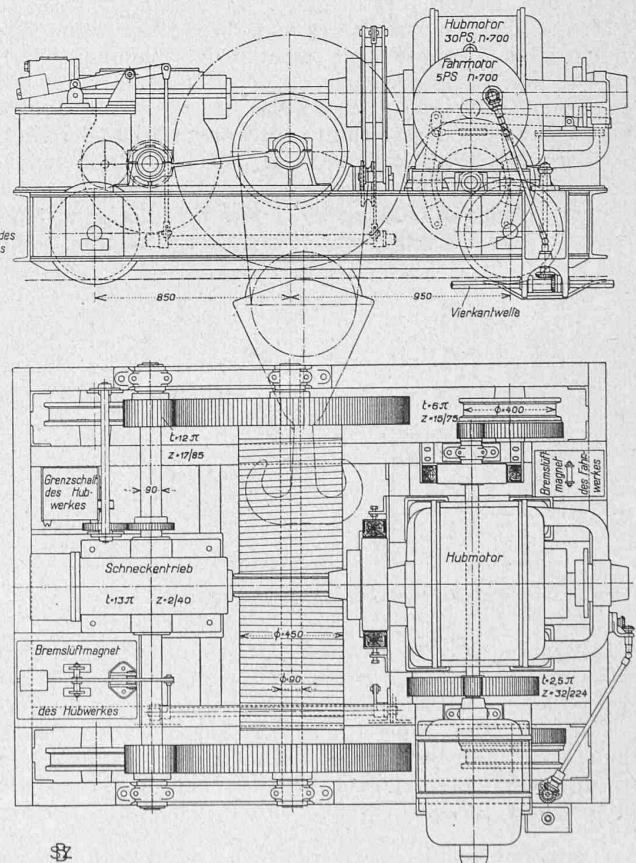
Laufwinde zum Kran in Abb. 22. — 1:30.
